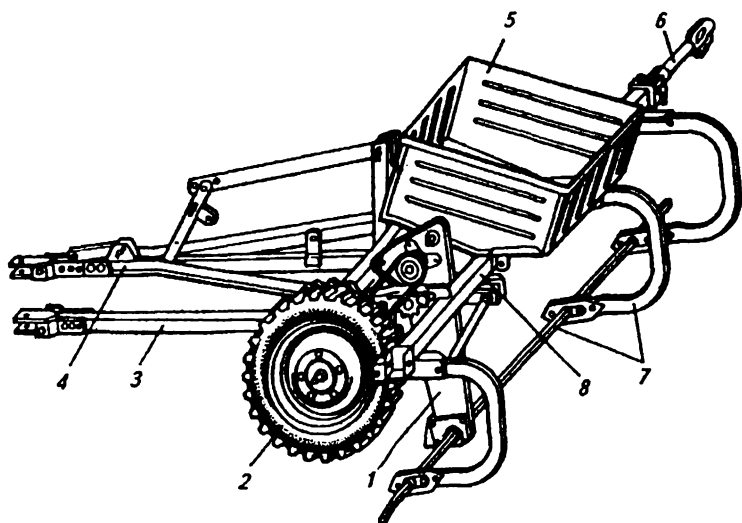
Штанговый культиватор КШ-3,6А: 1 — центральный грядиль; 2 — приводное колесо; 3 — тяга; 4 — прицеп; 5 — бункер; 6 — стяжка; 7 — грядиль со штангой; 8 — рама
